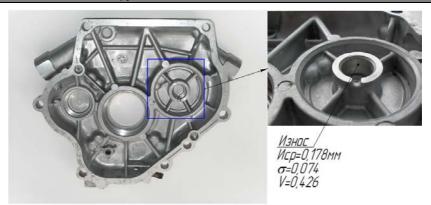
Изношенная поверхность под шейку кулачкового вала двигателя Briggs&Stratton модели 115400:
